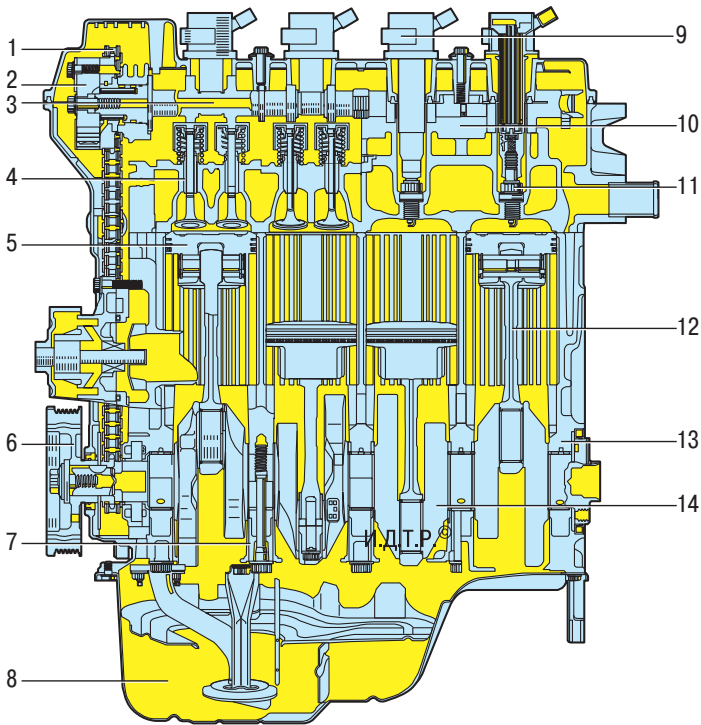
Двигатель 4ZZ-FE (продольный разрез): 1 – гидравлический клапан изменения фаз газораспределения; 2 – контроллер системы VVT-i; 3 – распределительный вал; 4 – клапан; 5 – поршень; 6 – шкив привода вспомогательных агрегатов; 7 – крышка коренного подшипника; 8 – масляный насос; 9 – катушка зажигания; 10 – постель распределительного вала; 11 – свеча зажигания; 12 – шатун; 13 – задний сальник коленчатого вала; 14 – коленчатый вал
